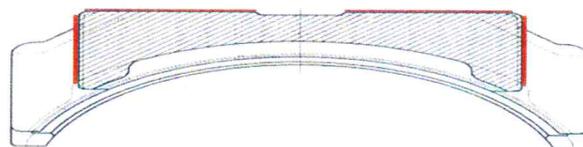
общий вид адаптера буксового узла колёсной пары
